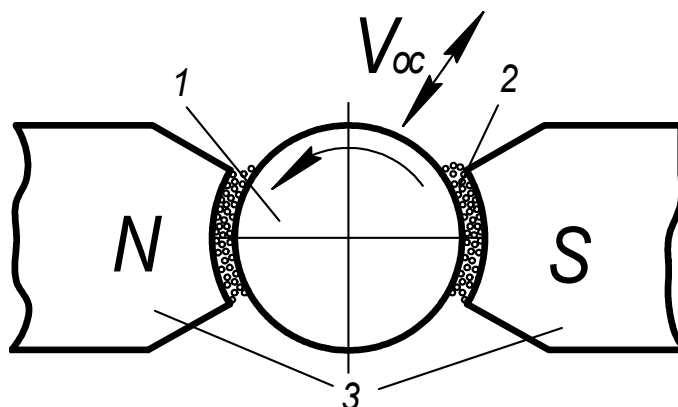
Схема магнитно-абразивной обработки цилиндрических поверхностей: 1 – обрабатываемая деталь; 2 – ферромагнитный порошок; 3 – полюсный наконечник
